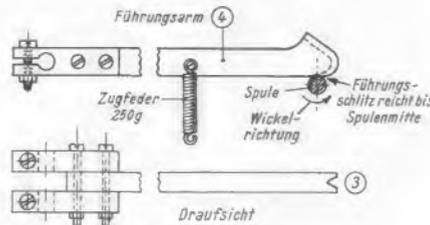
Der Drahtführungsarm mit dem Führungsschlitz daneben
